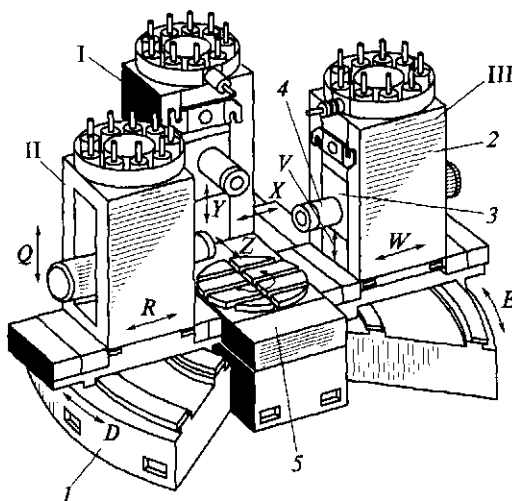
Агрегатный станок с ЧПУ с тремя силовыми головками: 1 — станина; 2 — стойка; 3 — силовая головка (шпиндельная бабка); 4 — шпиндель; 5 — крестовый стол; I, II, III — агрегаты
